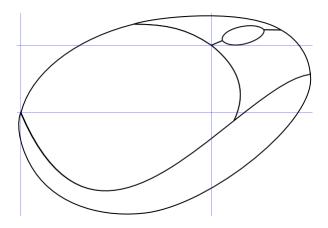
Построенный из отдельных сплайнов корпус мыши
